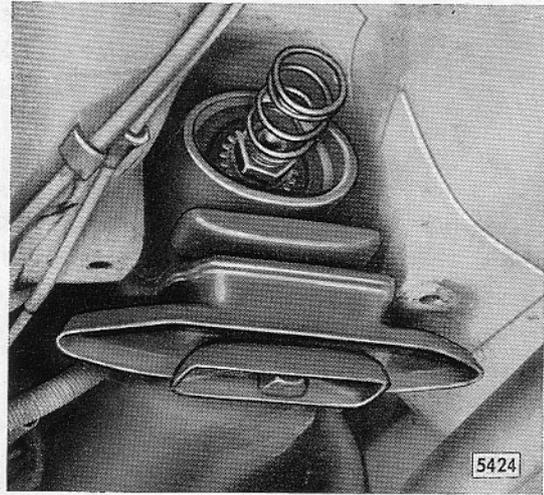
Druckfeder für Gelenkwelle auf Getriebehauptwelle aufgesteckt
